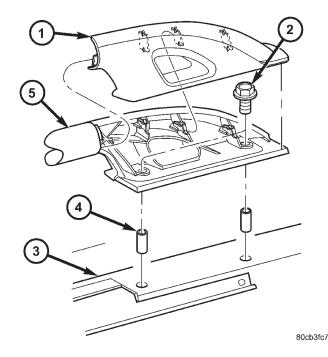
CUBIERTAS DE LOS PORTAEQUIPAJES
